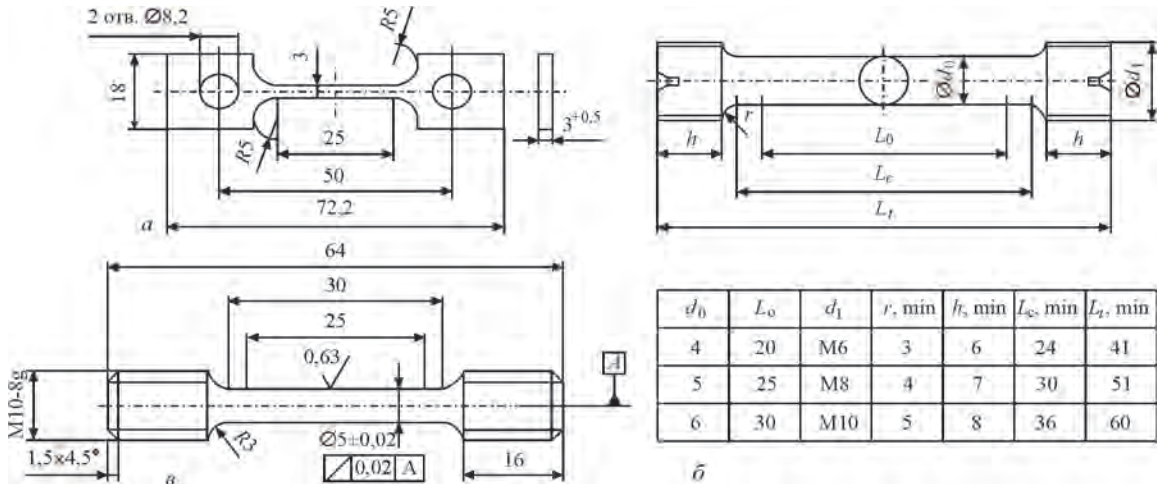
Зразки-прототипи, використані для конструювання оптимізованого плоского пропорційного мініатюрного зразка під задачу випробувань зварного з'єднання «основний-наплавлений метал» НЖС на високотемпературну тривалу міцність: а – плоский пропорційний зразок ІЕЗ ім. С.О. Патона; б – циліндричний зразок за ISO 6892-2:2011 [7]; в – циліндричний зразок для випробувань НЖС ВЖЛ12У та ЖС6У
